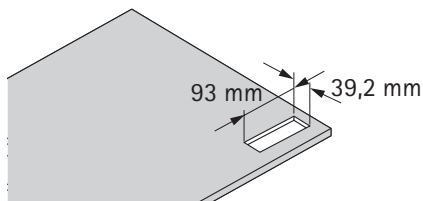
Fräsbild zum Einbau des Handschalters LegaDrive Touch Inlay mit Gummilamellen
